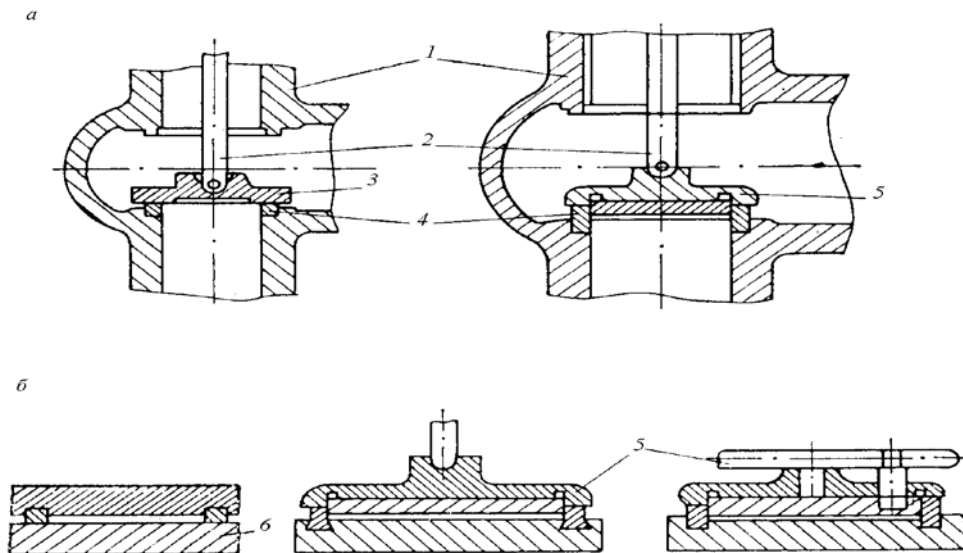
Конструкции притиров для притирки уплотнительных поверхностей дисков, клиньев и корпусов задвижек:
